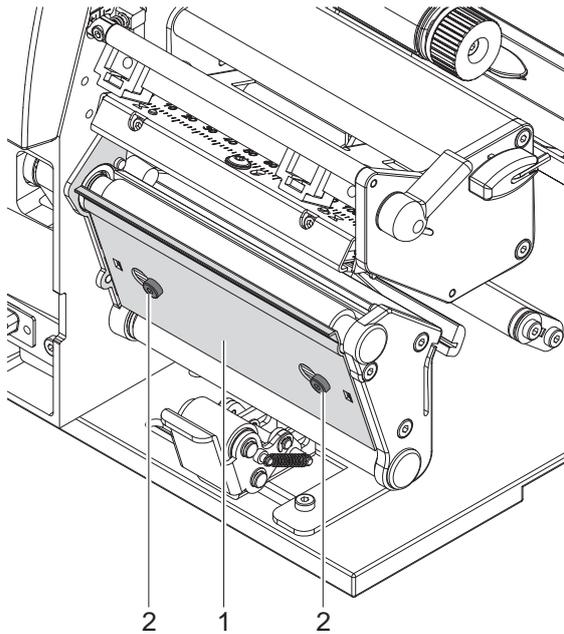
Démontez et installez la tôle de rembobinage, de pré-décollement ou d'arrachage.
